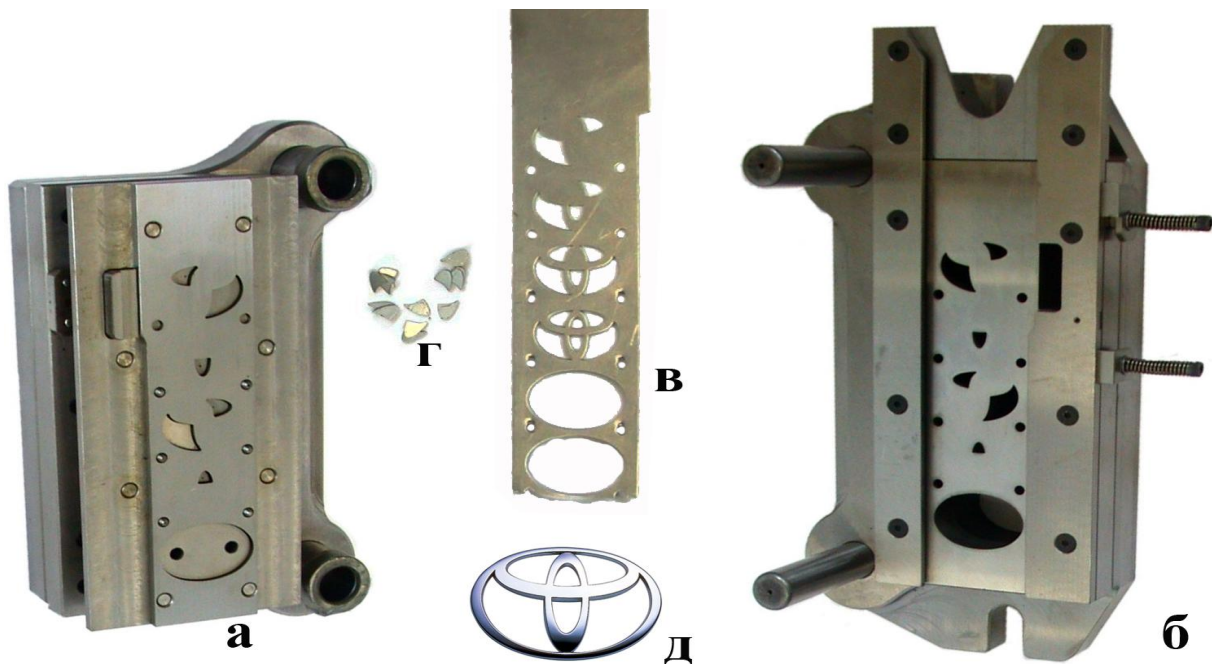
Листовий штамп для виготовлення логотипу автомобіля Toyota: а – верхній штамп; б – нижній штамп; в – листова заготовка; г – відходи металу; д – виріб.
